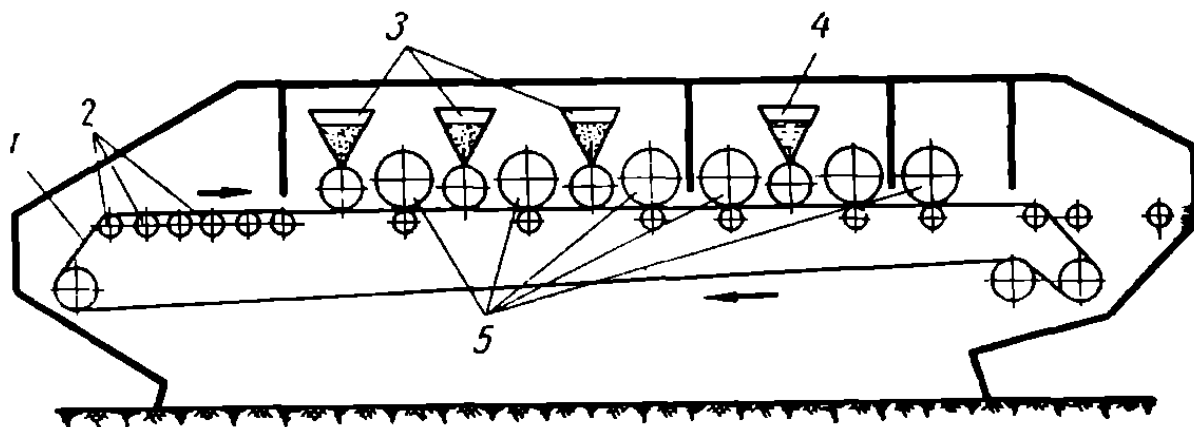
Схема располировочного агрегата для совмещенного выполнения операций шлифования и полирования лаковой пленки
